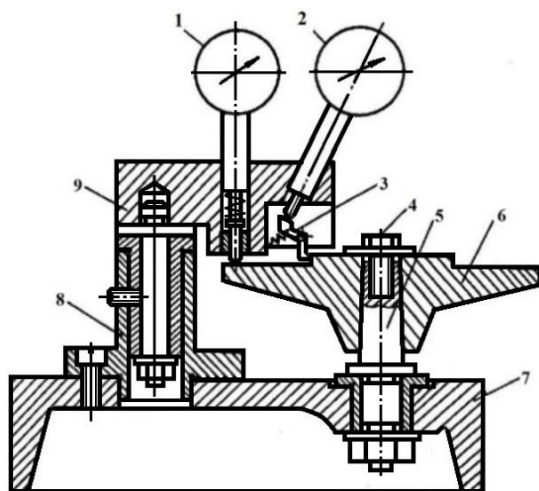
Приспособление для контроля торцевого и радиального биения
